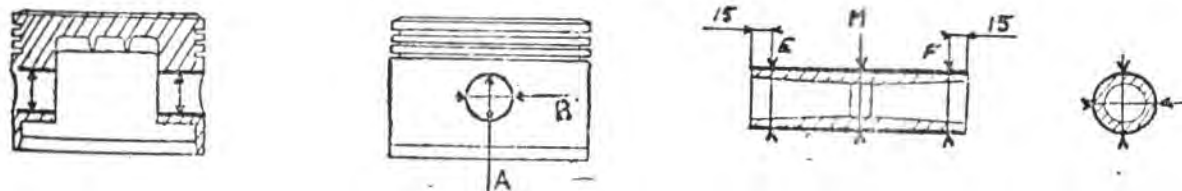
MENSURATIONS DES PISTONS ET AXES DE PISTON
